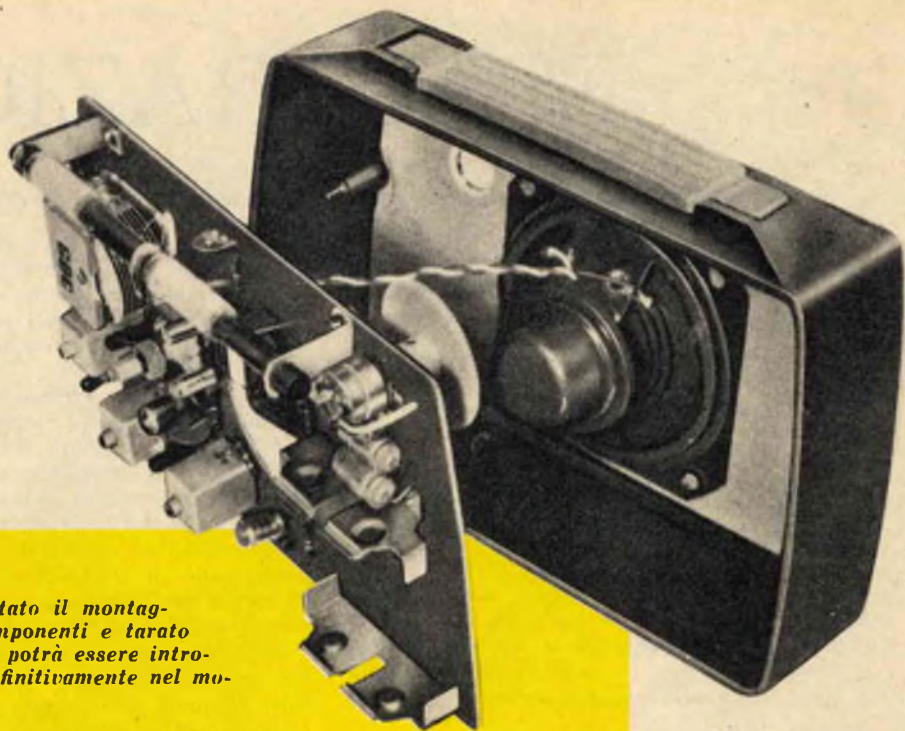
Completato il montaggio di tutti i componenti e tarato il ricevitore, esso potrà essere introdotto e fissato definitivamente nel mobile.
